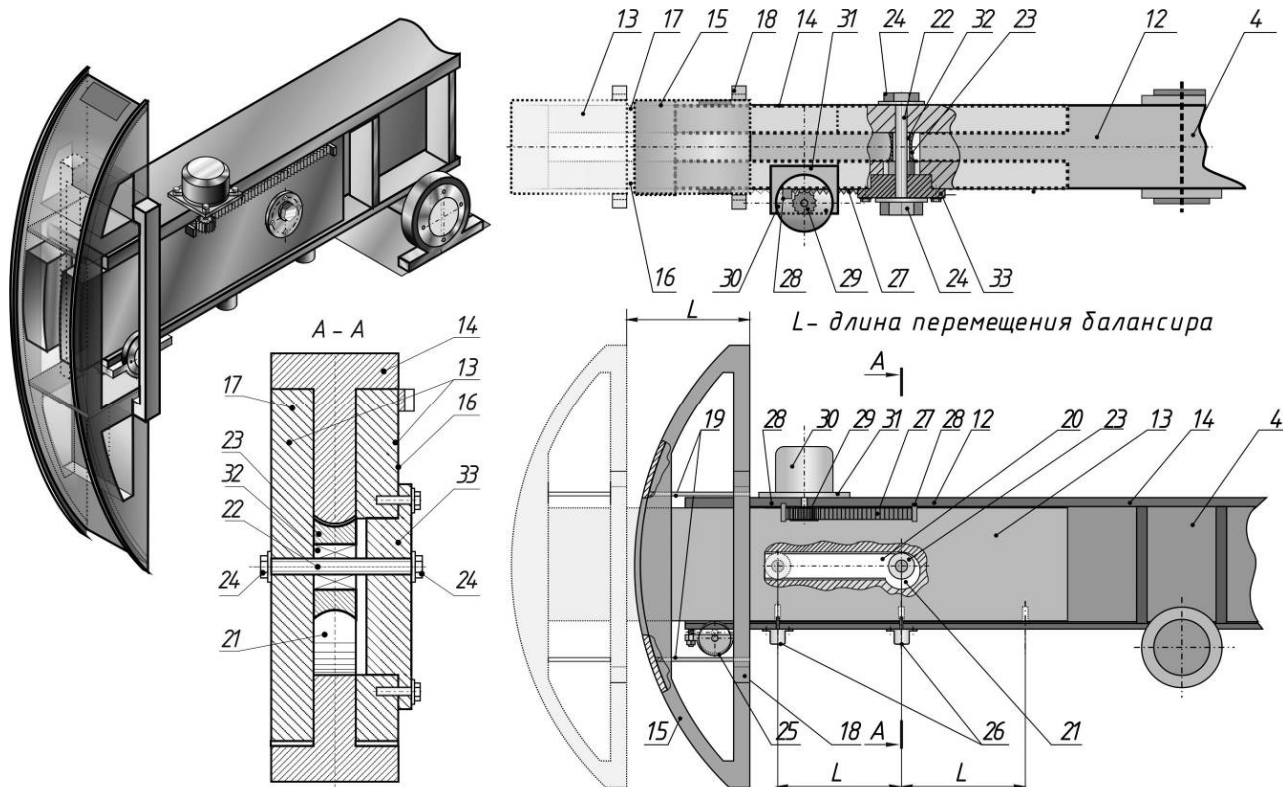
Усовершенствованная конструкция балансирного привода штанговой скважинной насосной установки
